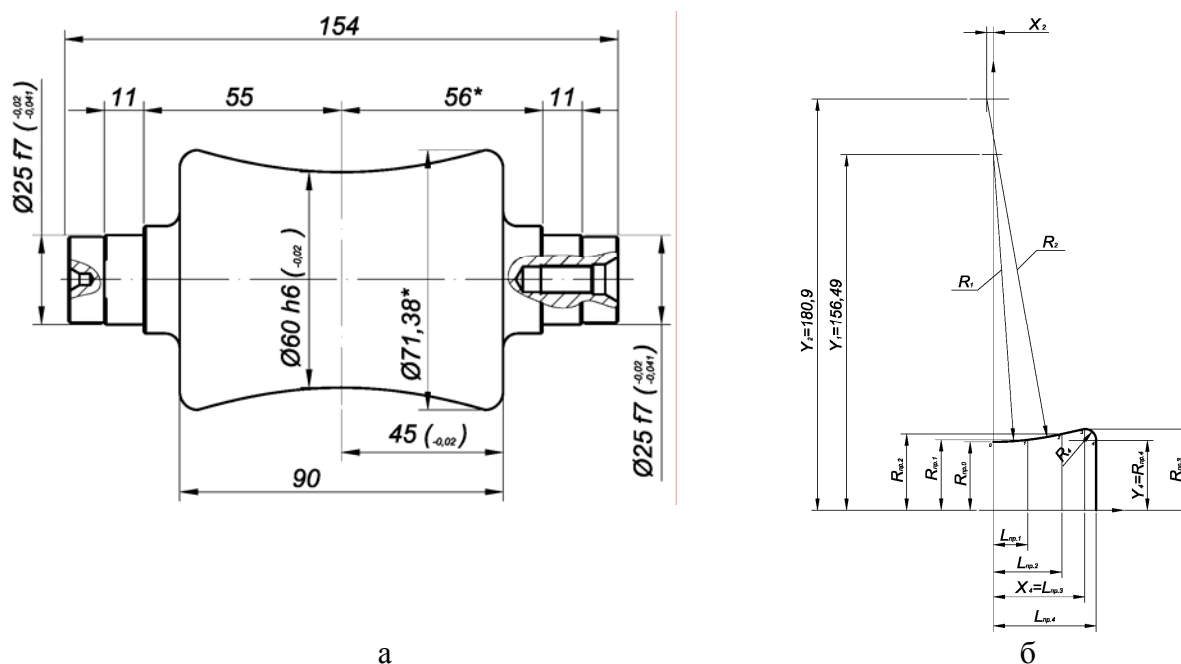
Калибровка рабочих валков, а – общий вид валка, б – профиль бочки валка
